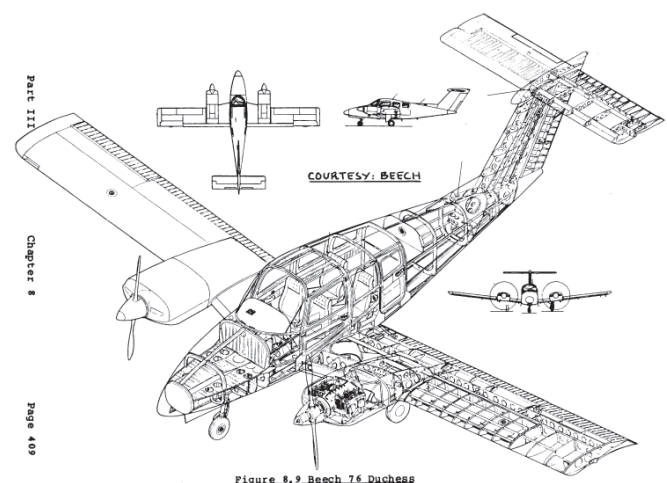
Plan de l'arrangement structurel d'un Beech 74 Duchess
